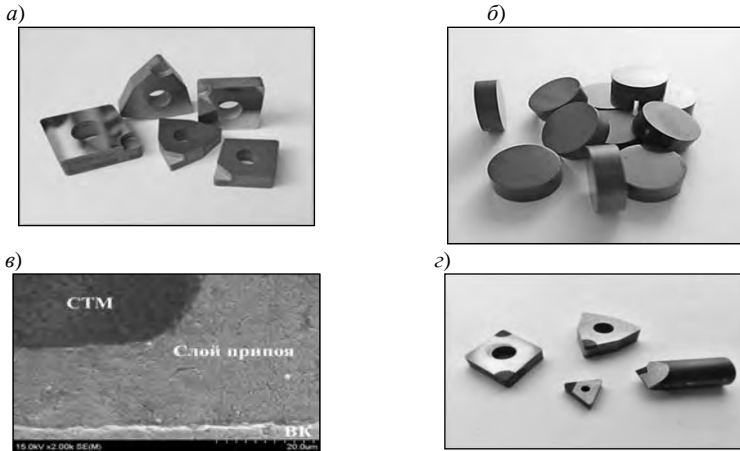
Твердосплавные пластины различной конфигурации после электроэрозионной обработки (а); внешний вид режущих элементов из CTM (б); соединение твердосплавной режущей пластины и керамического режущего элемента из CTM ($\times 2000$) (в); режущие вставки после механической обработки (з)
